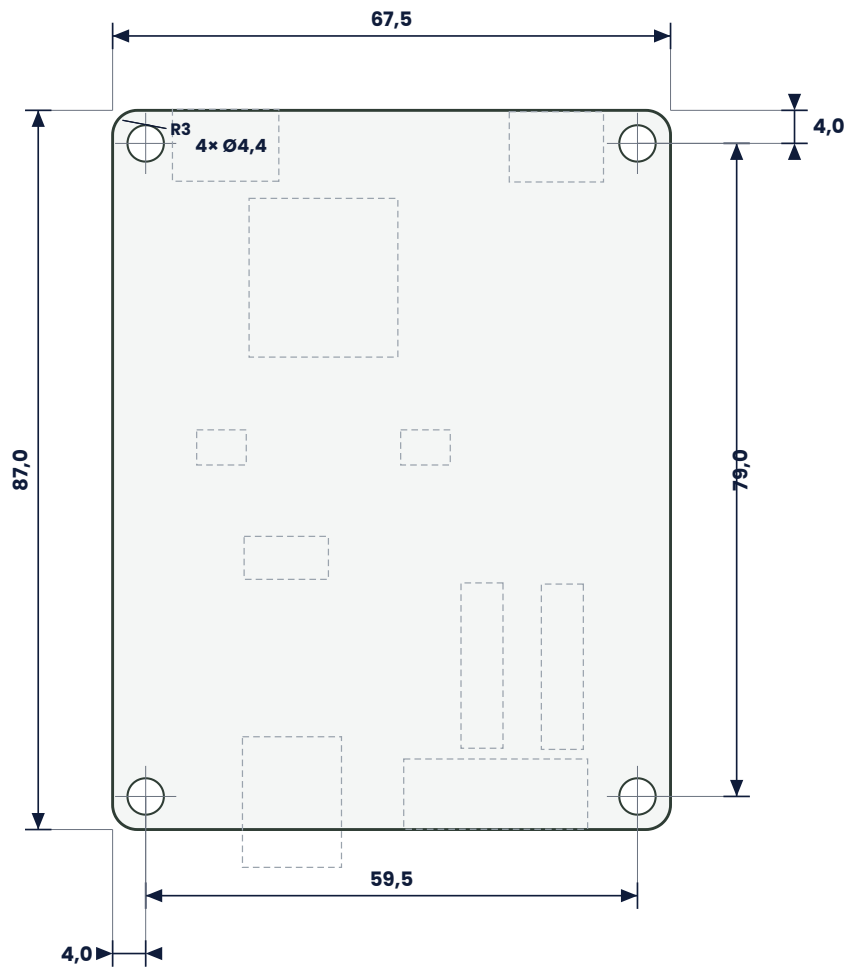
Dimensiones de la tarjeta y posición de los orificios de montaje. Cotas en mm.
